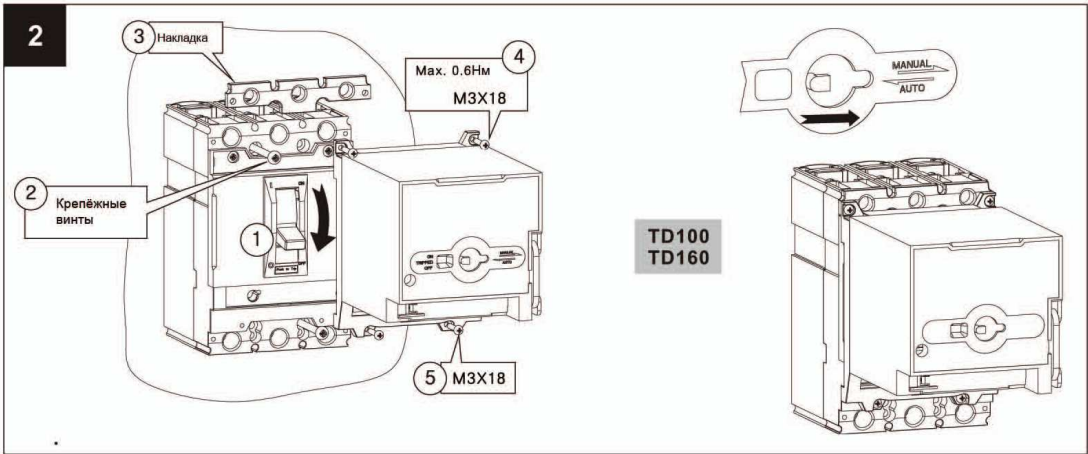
Установка моторного привода на выключатели TD100 и TD160
